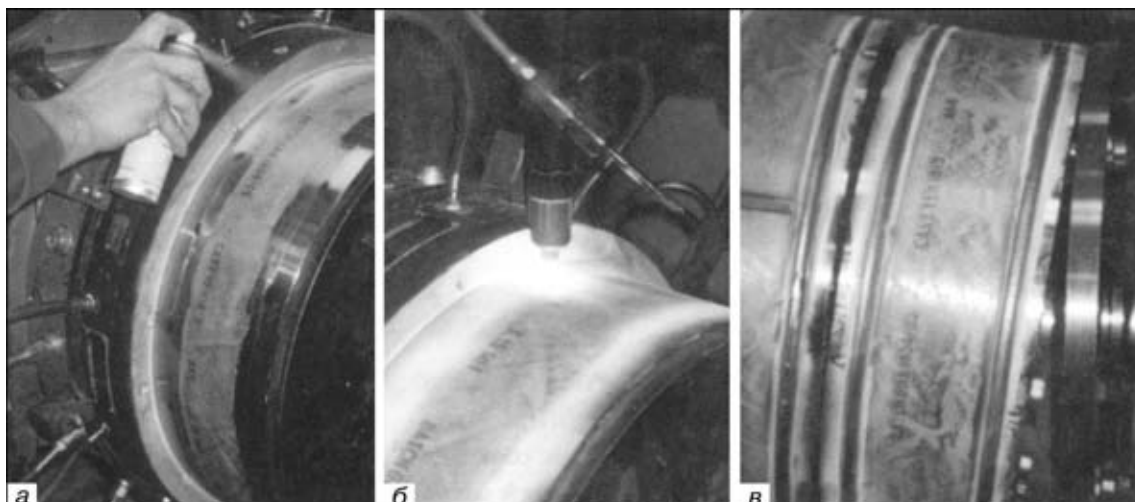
Сварка элемента цилиндрического корпуса газотурбинного двигателя из никелевого сплава Нимоник-75 толщиной 3,25 мм [16] способом А-ТИГ: а — нанесение аэрозольного активатора на стык перед сваркой вручную; б — механизированный способ сварки А-ТИГ; в — сварной шов
